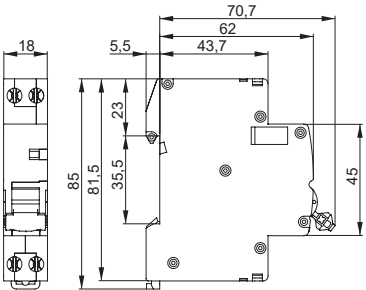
Габаритные и установочные размеры АВДТ / Figure 4 – Overall and mounting dimensions of RCBO
